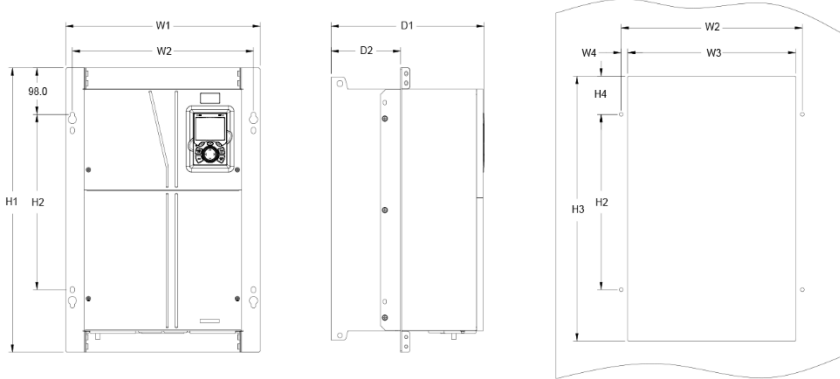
Схема ПЧ для фланцевого монтажу 660 В, від 22 до 132 кВт
